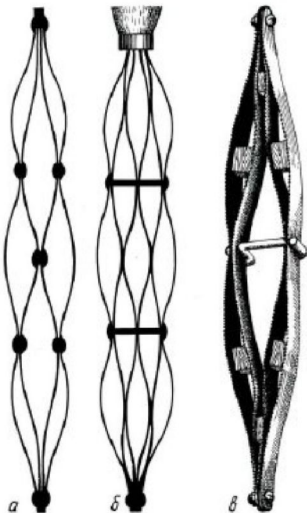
Изготовление пилорашпиля из ножовок для металла: а) и б) на заклёпках или болтиках; в) на металлических и деревянных распорках
